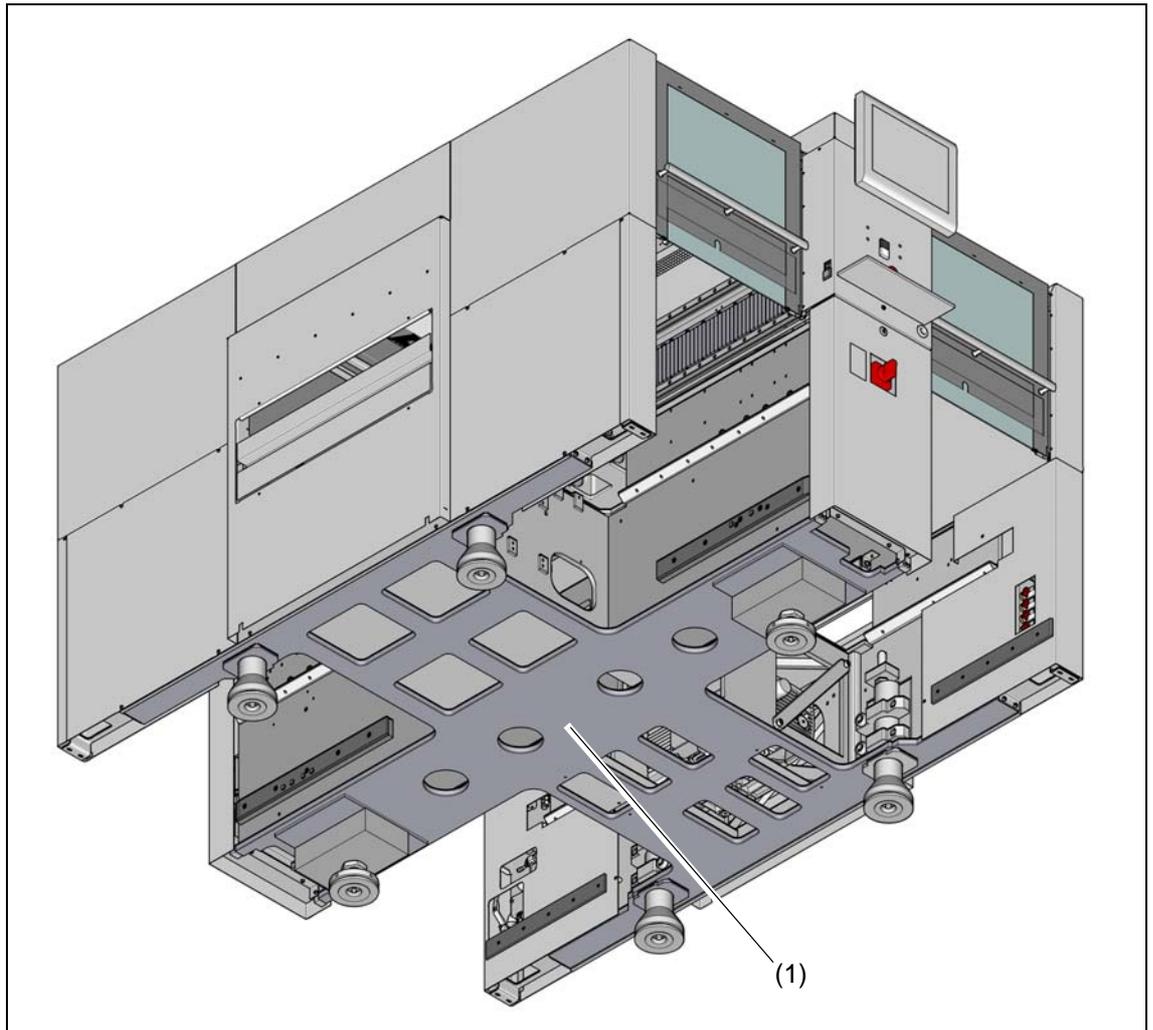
4 接触表面 - 与 PCB 传送方向平行的货叉 (示例为 SX4)
